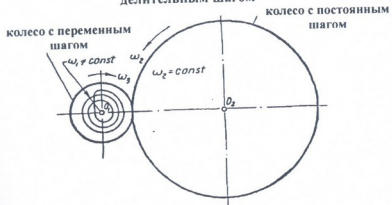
Цилиндрическая зубчатая передача с переменным делительным шагом
